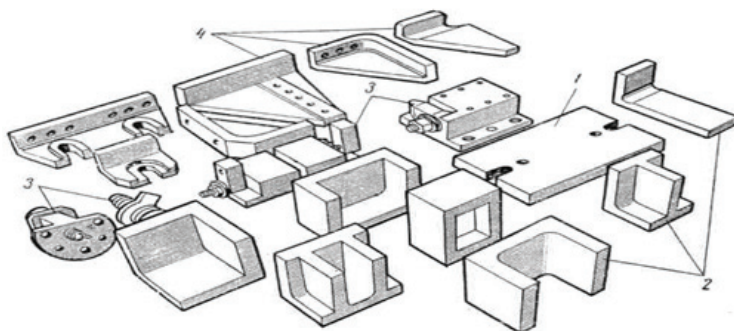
Унифицированные детали и узлы сборно-разборных приспособлений
